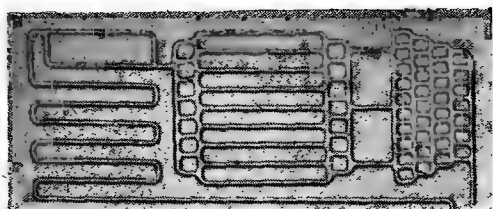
Прокатно-сварной теплообменник.
